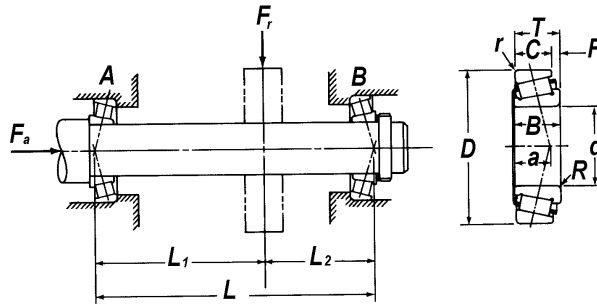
8 Montaje De Un Par De Cojinetes De Rodillos Cónicos
